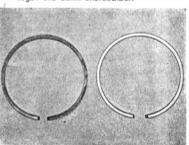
Die Ringflanken müssen blank sein und gleichmähige Färbung zeigen (rechter Ring). Bei ungleichmähiger Färbung ist der Ring verzogen (linker Ring).
